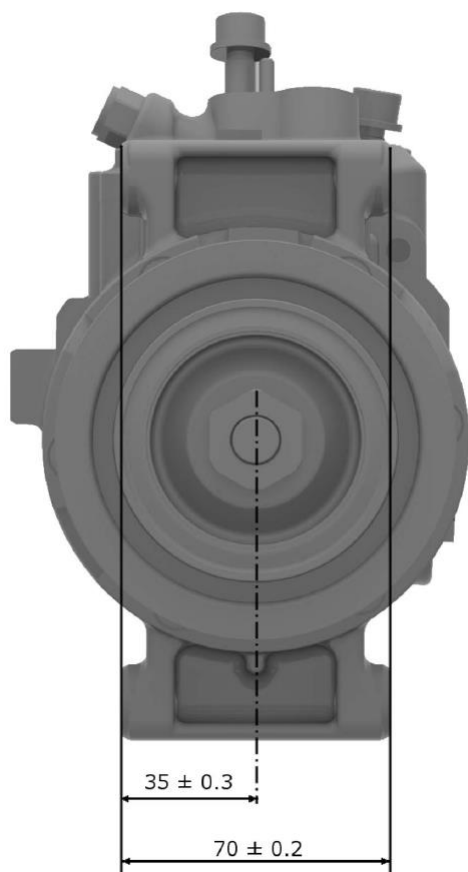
Размеры компрессора климатической установки DENSO-7SEU17, диаметр шкива 100 мм (вид спереди)
